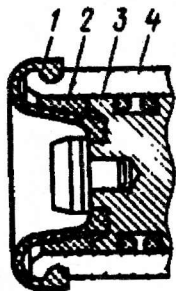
Установка пенополиуретановых колец в колесные цилиндры:
